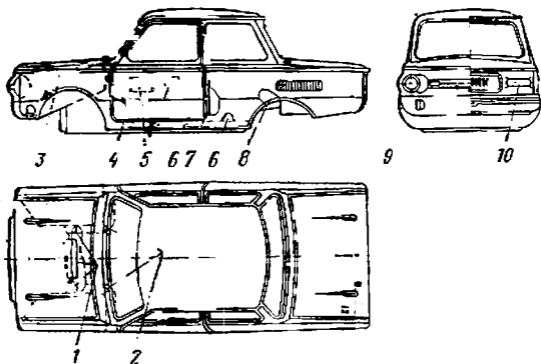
Схема мест дополнительной противокоррозионной обработки кузова ЗАЗ-968
